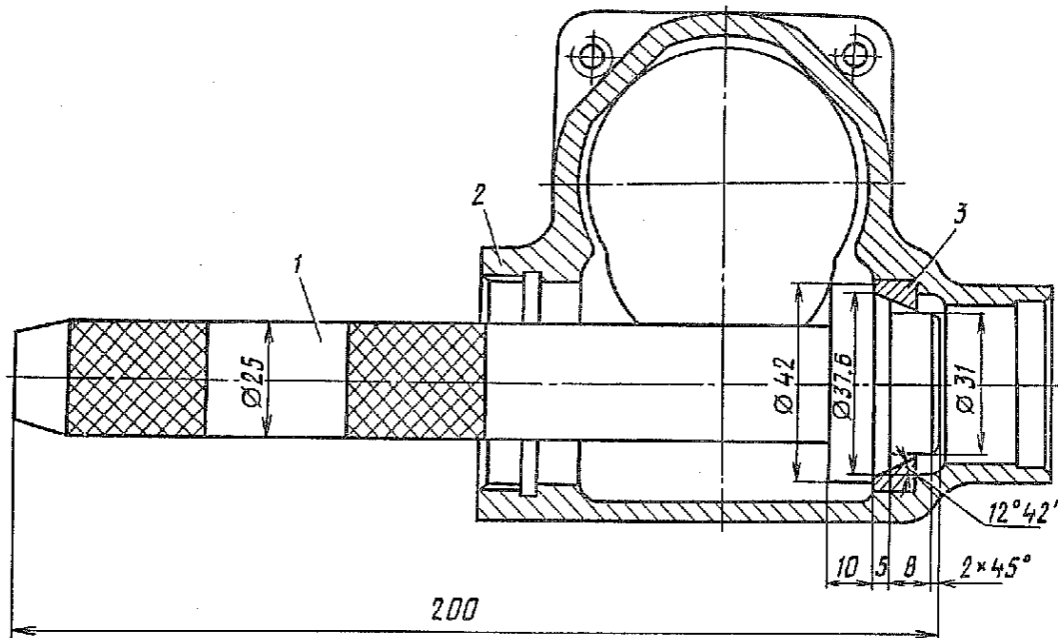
Запрессовка наружного кольца подшипника червяка рулевого управления:
